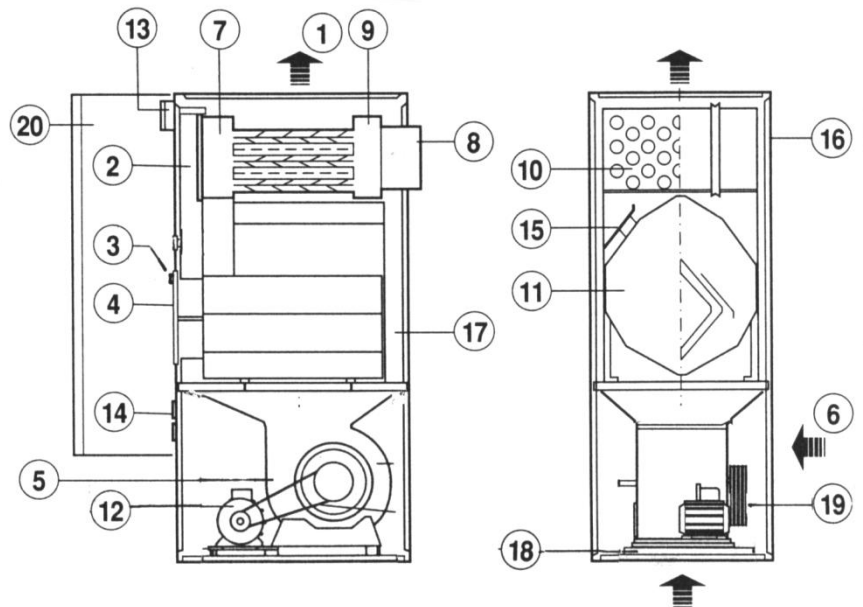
Воздухонагреватель серии LGE (сверху) и воздухонагреватель серии LGE OUT (внизу)
